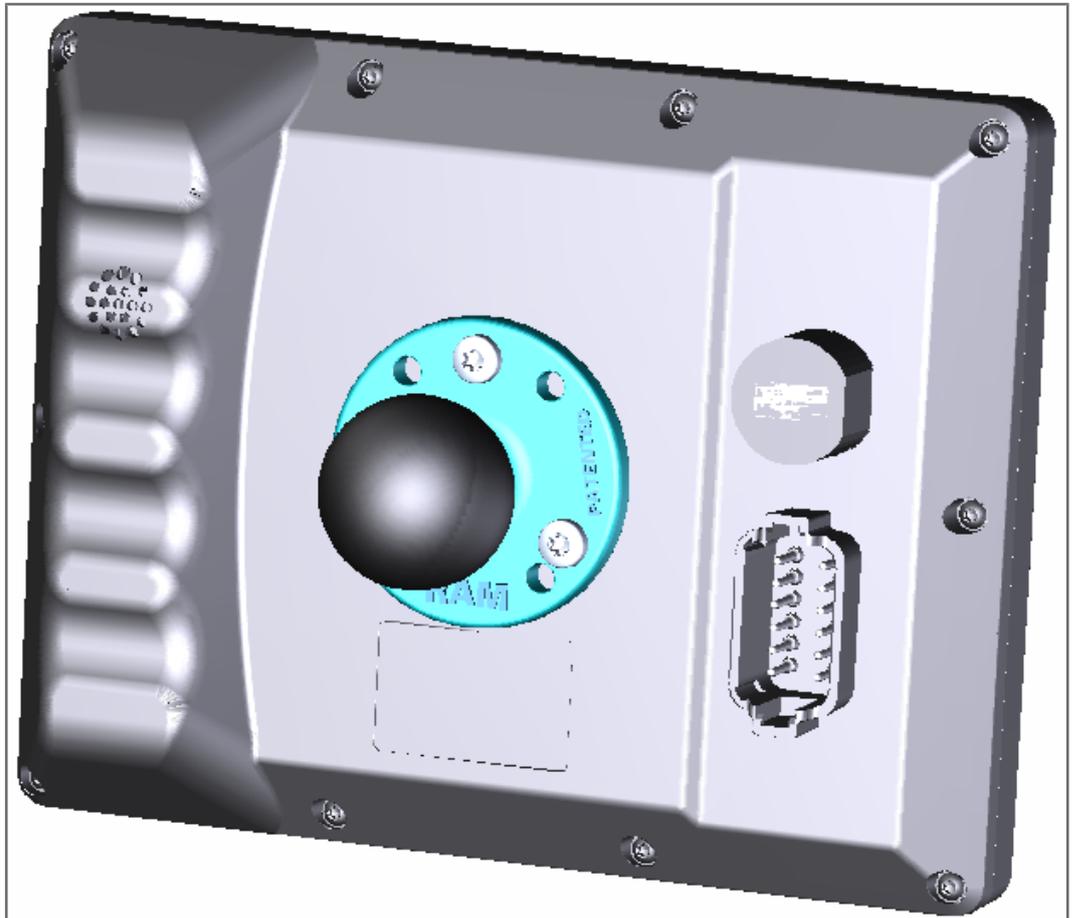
Erlaubte Einbaulage mit RAM-Mount-Halterung
